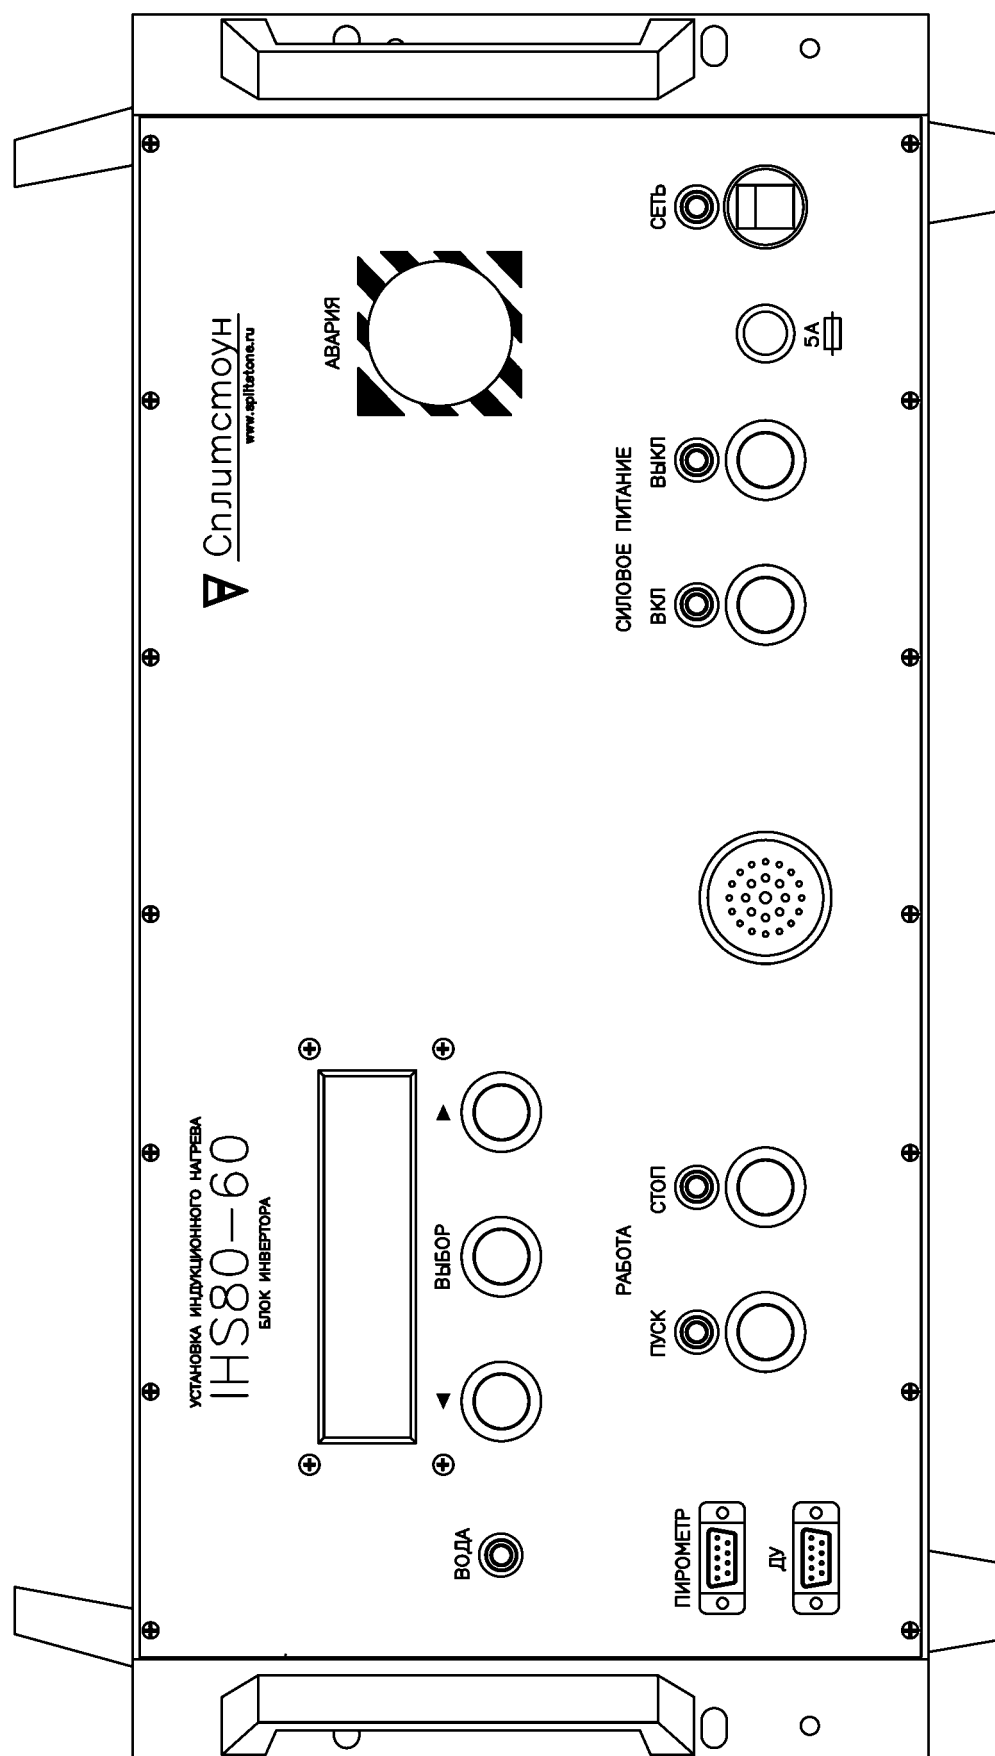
Блок инвертора IHS 80-60. Вид спереди
